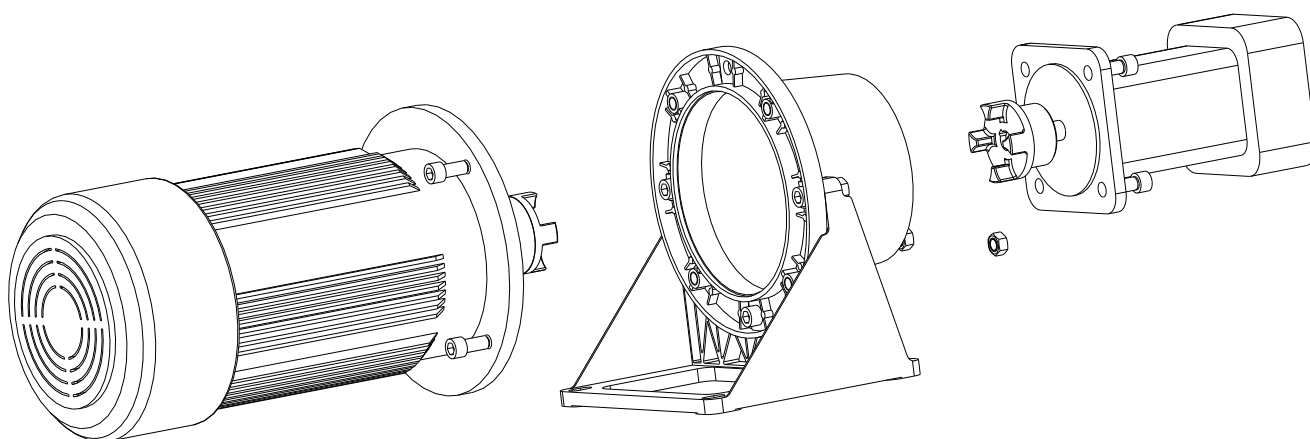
Montaggio motore elettrico e/o pompa con lanterna e flangia base
